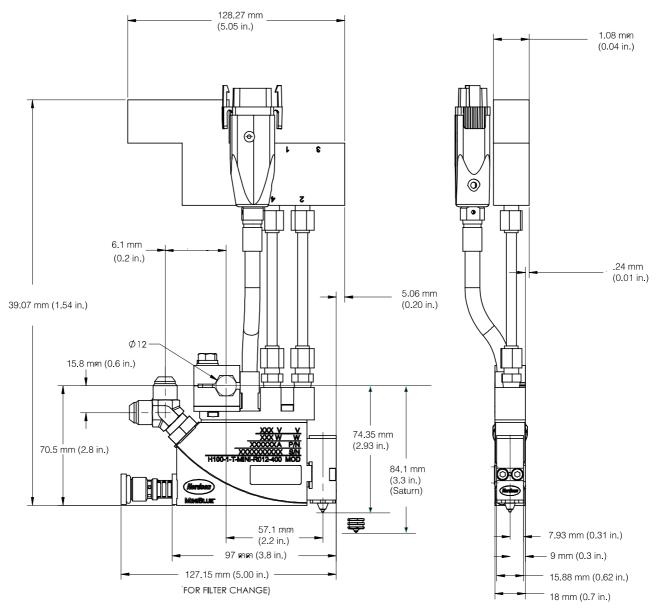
Dimensioni di una pistola sottile a modulo singolo con elettrovalvola SG
